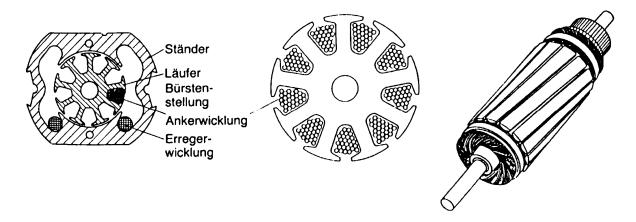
Querschnitt durch Universalmotor, rechts Ansicht Rotor Abbildung aus Skript H. Burtscher [Bu]
